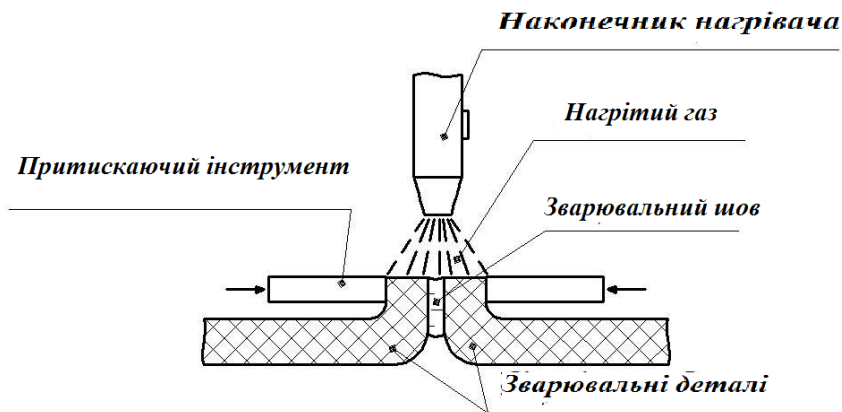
Зварювання нагрітим газом без присадочного матеріалу
